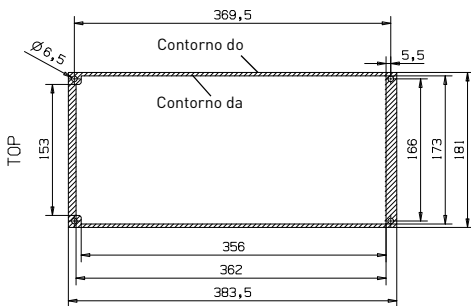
Dimensões do recorte para montagem com flange do MR4 ao MR6 (unidade: mm)
